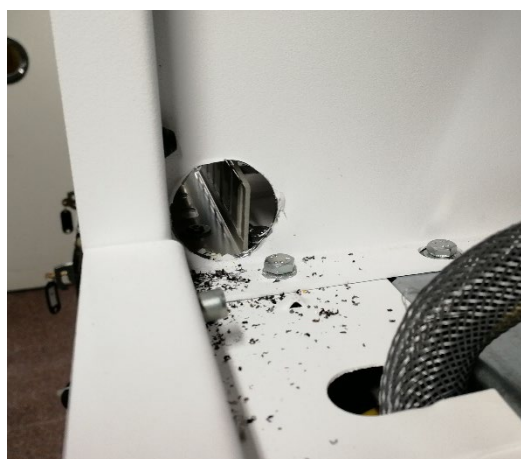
Orificio practicado al lateral izquierdo del ACP para facilitar el cableado.
